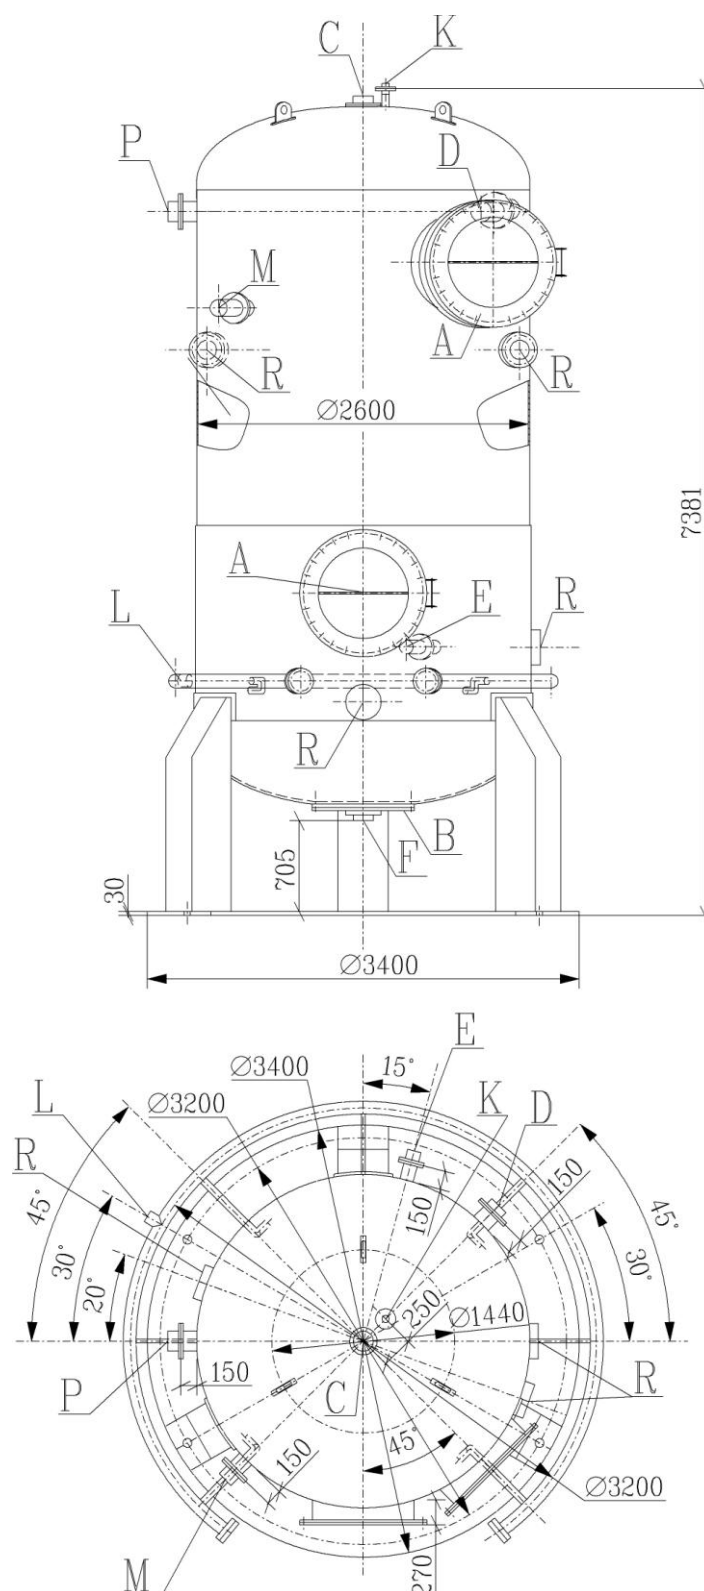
Габаритный чертеж фильтра-регенератора катионита LDP43AT001
